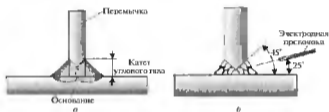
Сварка таврового соединения в нижнем положении
